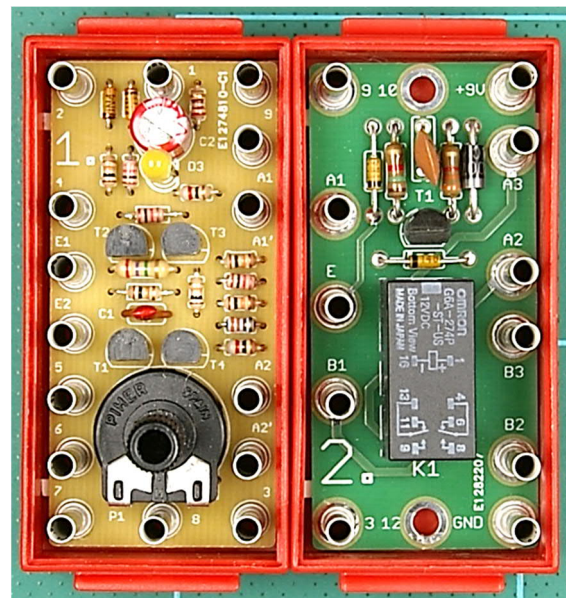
Platinen 26 mm · 56 mm doppelseitig
